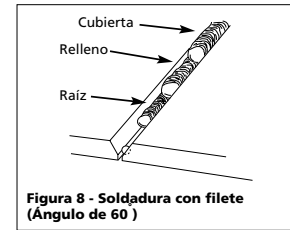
Soldadura con filete (Ángulo de 60°)
